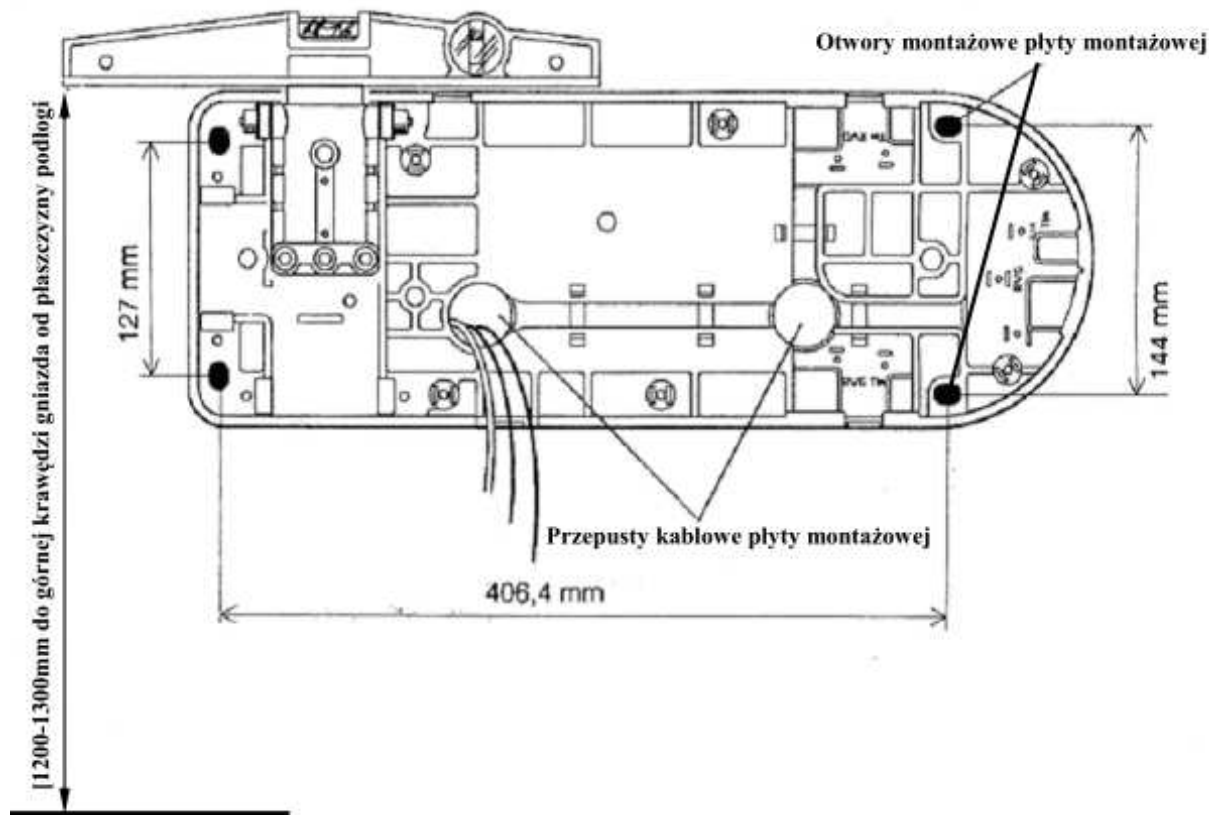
Aparat opcja z pionowo instalowaną płytą montażową ramienia poziomego
